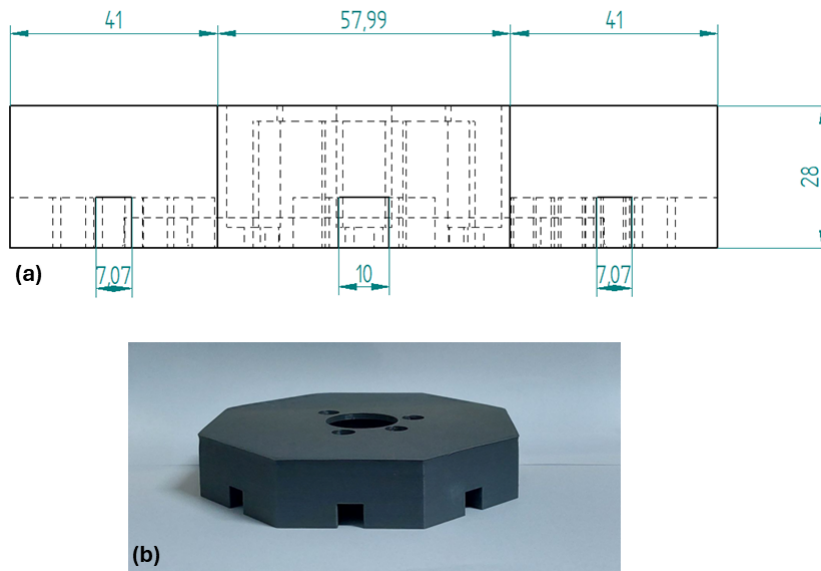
Vista frontal da peça central: (a) Desenho técnico (b) Peça impressa.
